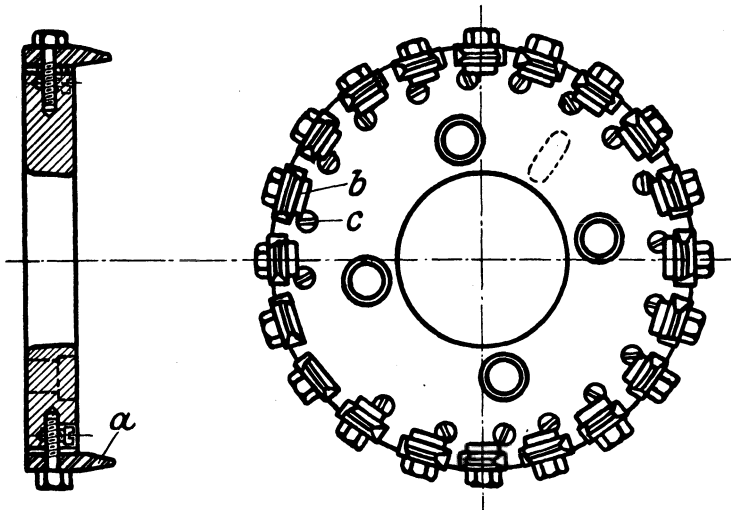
Messerkopf der Gleason-Kegelradfräsmaschine.
